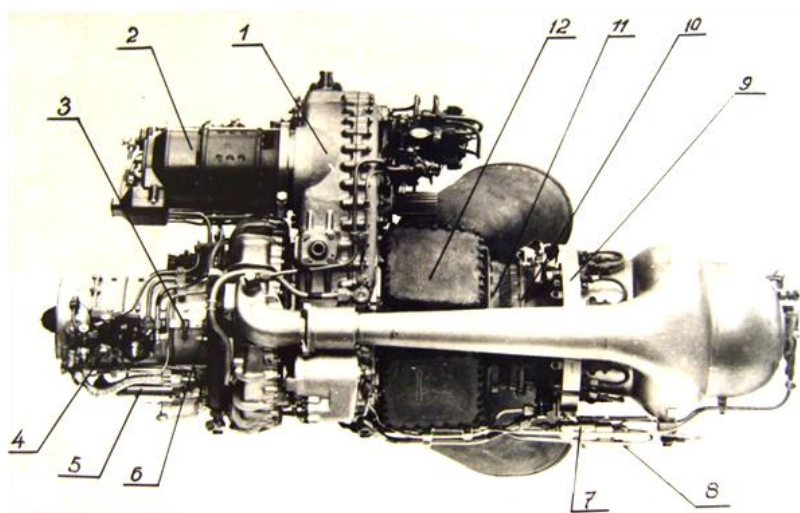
Двигатель ГТД-350 (вид слева)
